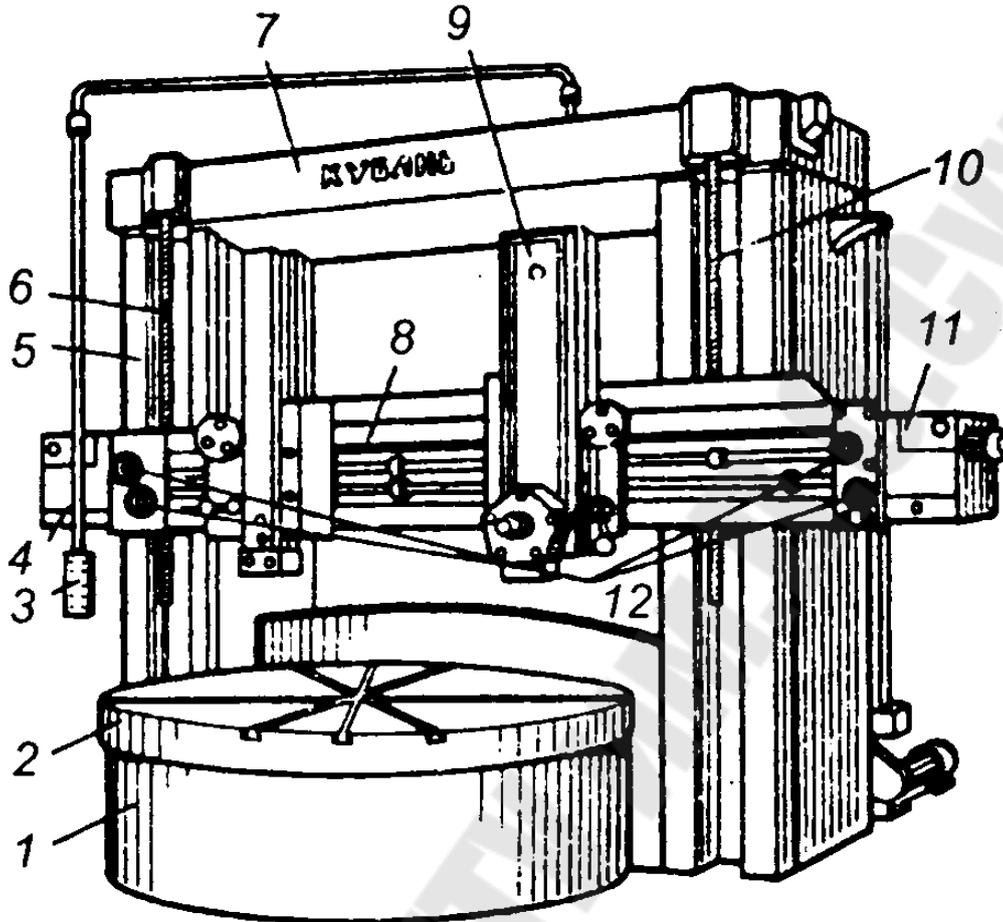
Общий вид токарно-карусельного двухстоечного станка
